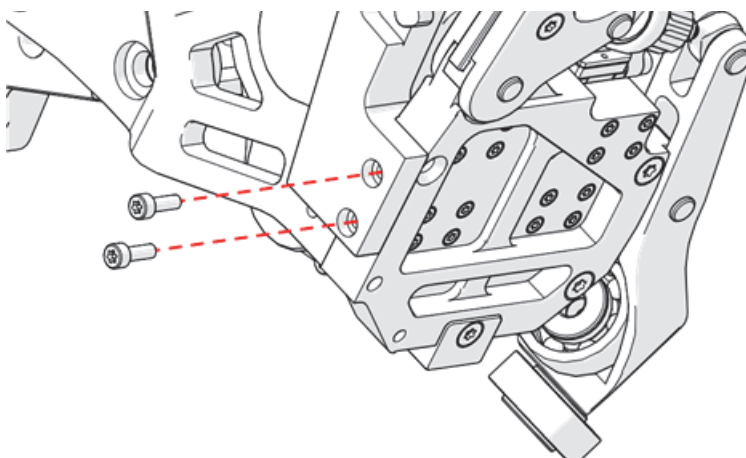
Retire los tornillos del brazo del transportador de motor
